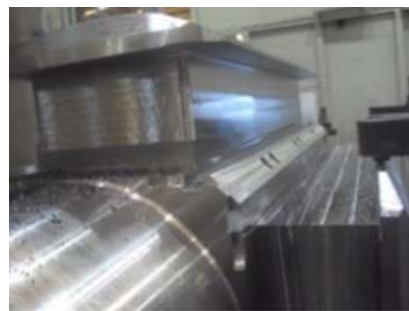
Usinagem dos polos do rotor do motor síncrono linha SM40
